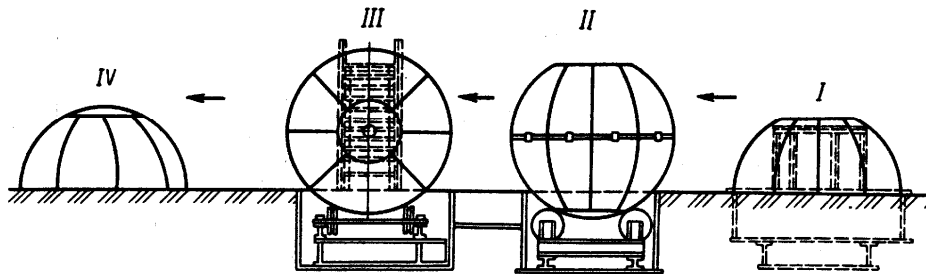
Схема технологического процесса сборки и сварки днищ газгольдеров
